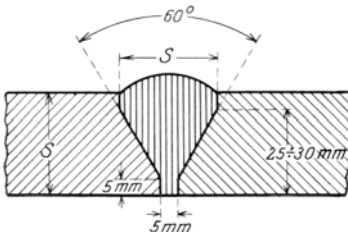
Bearbeitung der Schweißmulde ohne Stiftsetzung.
